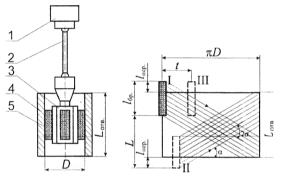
Схема установки хона в процессе хонингования: I — шпиндель станка; 2 — шарнирное устройство; 3 — хонинговальная головка; 4 — гильза; 5 — хонинговальный брусок; 2α — угол скрещивания следов; α — угол подъема следа; I, II, III — последовательные положения бруска за один двойной ход
